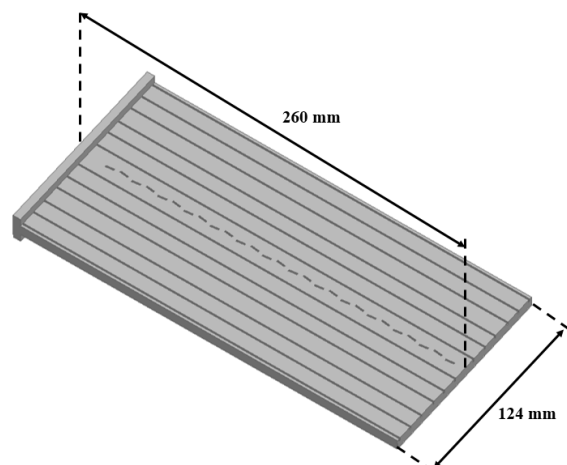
SWAA com fendas inclinadas e ranhuras metálicas.
